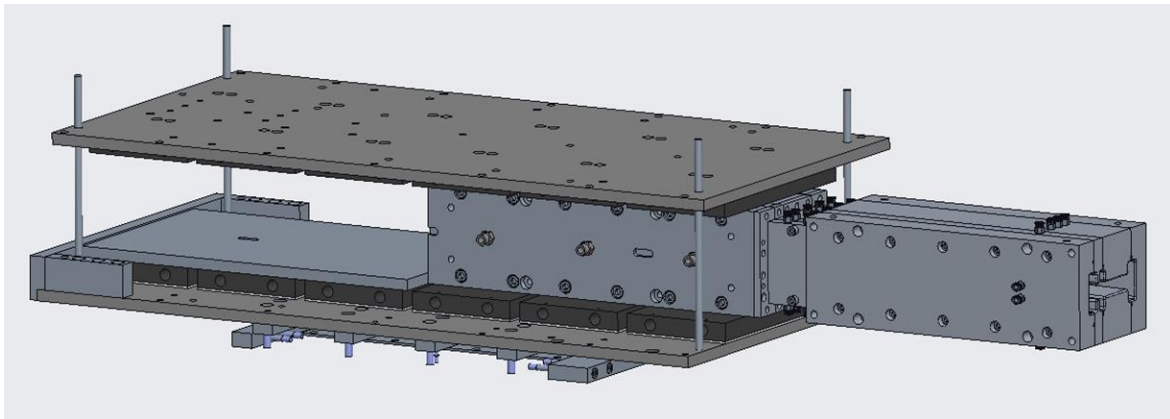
Einbau des Werkzeugsystems in den Werkzeugträger
